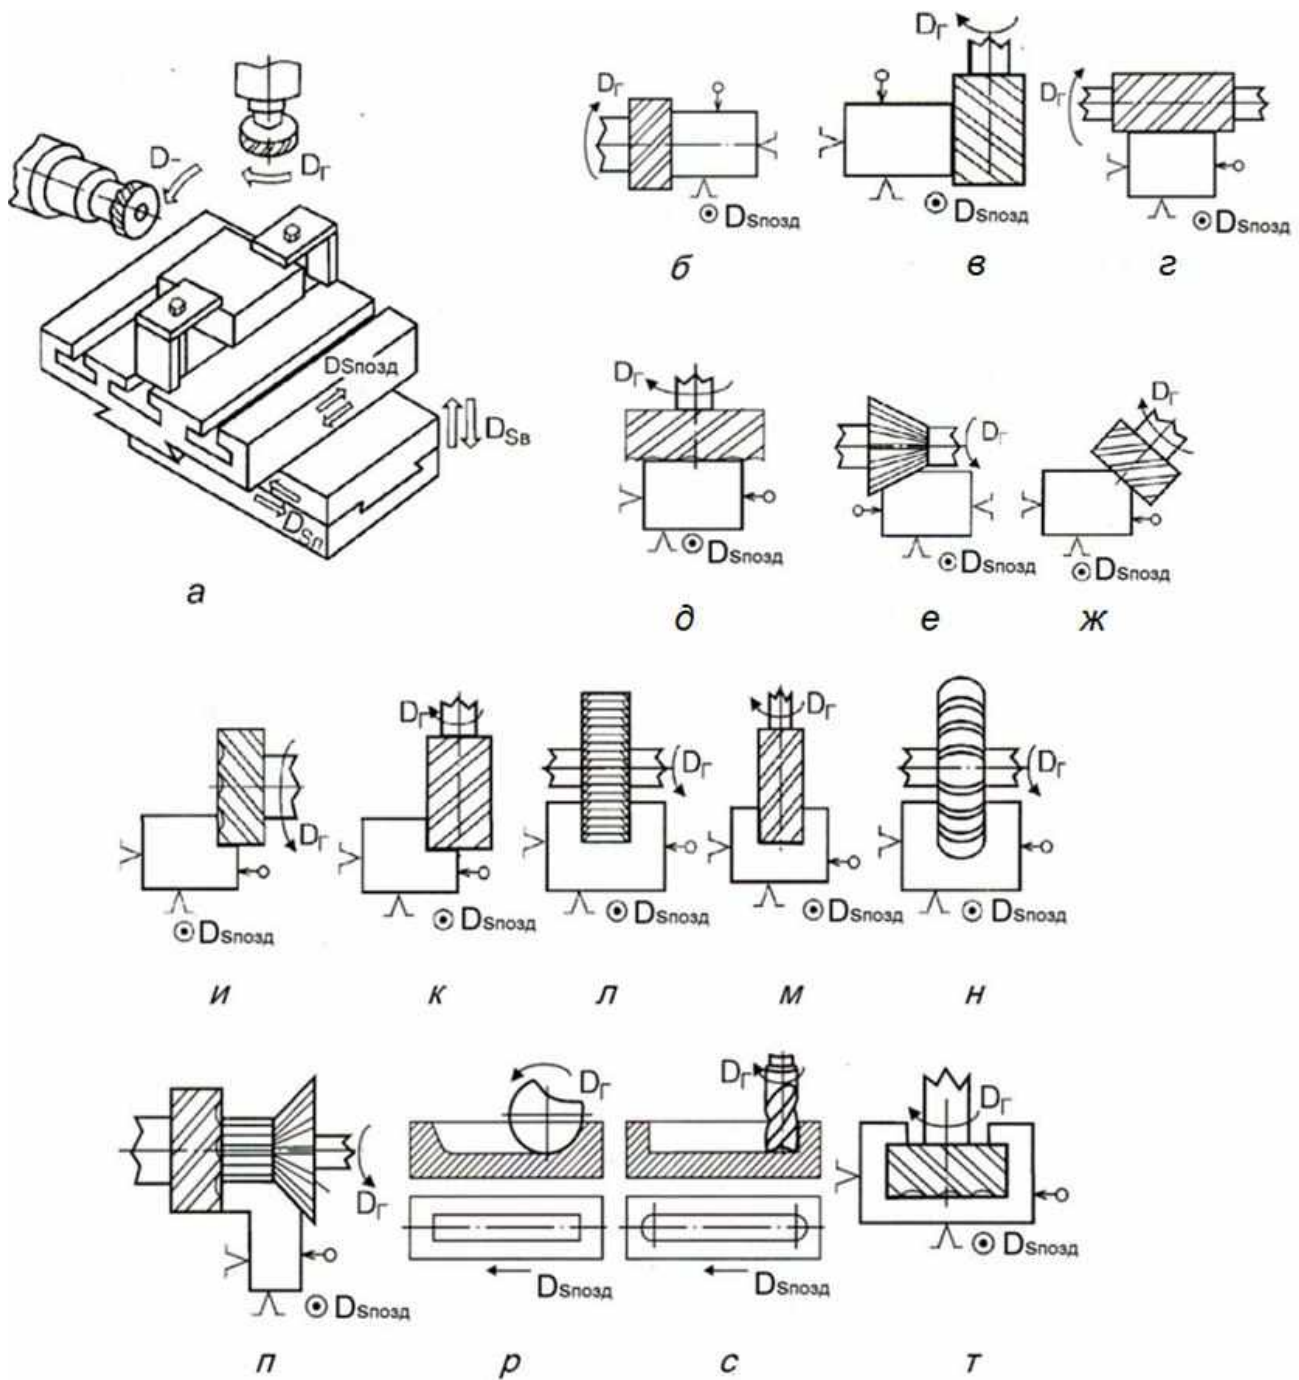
Закріплення заготовки на столі (а) і схеми оброблення поверхонь на універсальних фрезерних верстатах: б, в – фрезерування вертикальної площини; г, д – фрезерування горизонтальної площини; е, ж – фрезерування похилої площини; и, к – фрезерування уступу по двох площинах; л, м – фрезерування прямокутного паза; н – фрезерування криволінійного паза; п – одночасне фрезерування трьох поверхонь; р, с – фрезерування шпонкового паза дисковою й пальцевою фрезами; т – фрезерування Т-подібного паза
